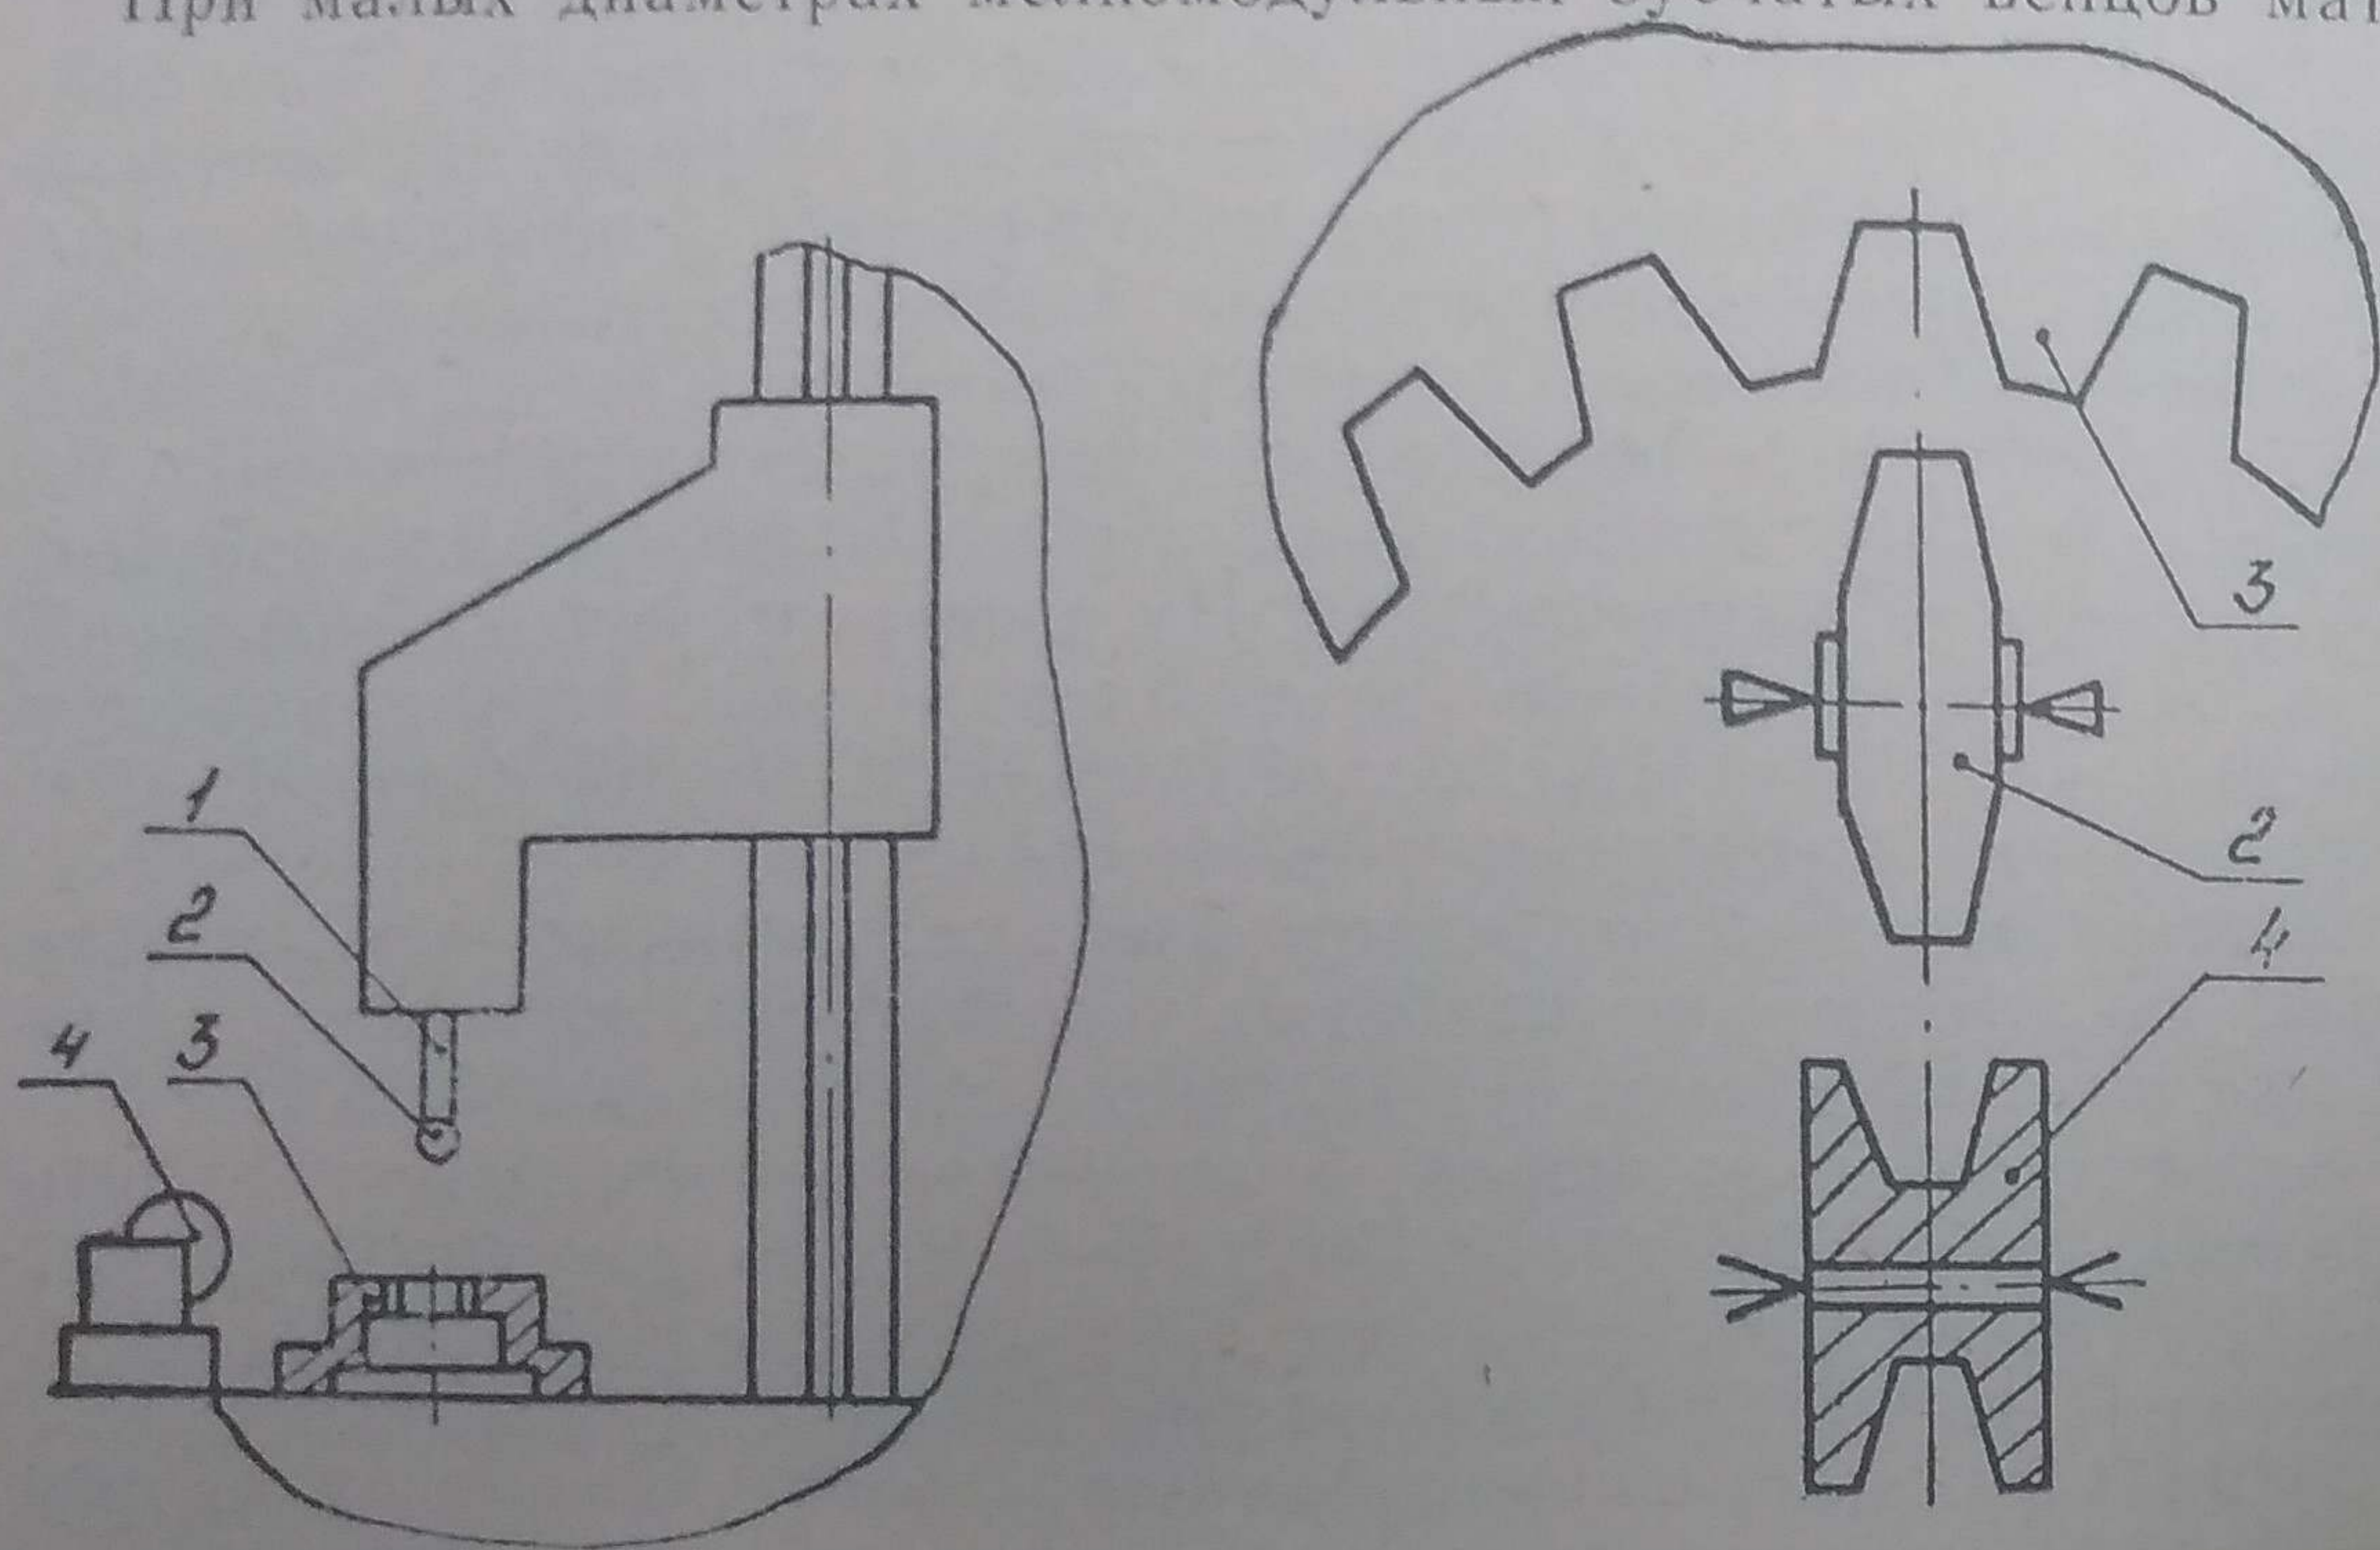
Схема обработки зубчатого венца на координатношлифовальном станке:
